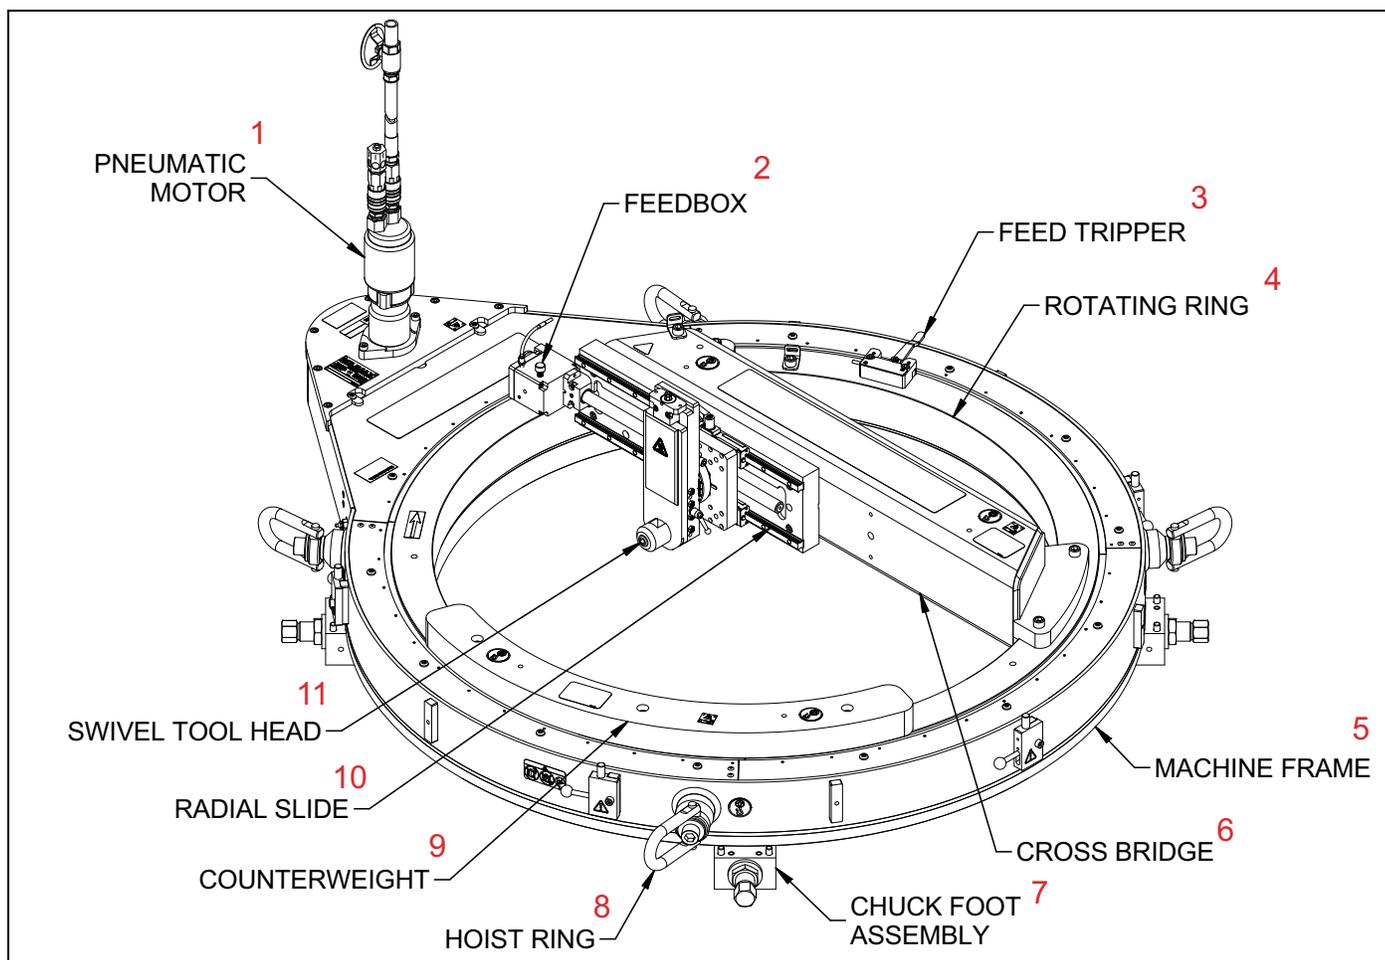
COMPOSANTS TYPES DE LA MACHINE SPEED FACER (MODÈLE ODF40 ILLUSTRÉ)
